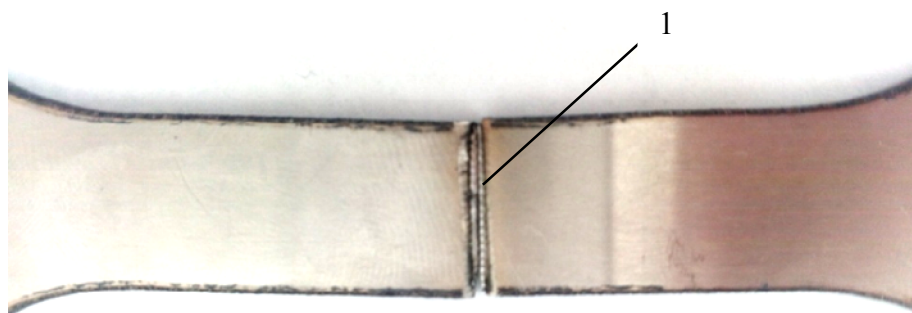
Образец сварного соединения стали 12X18H10T после испытания на разрыв: 1 – место разрыва образца при растяжении
